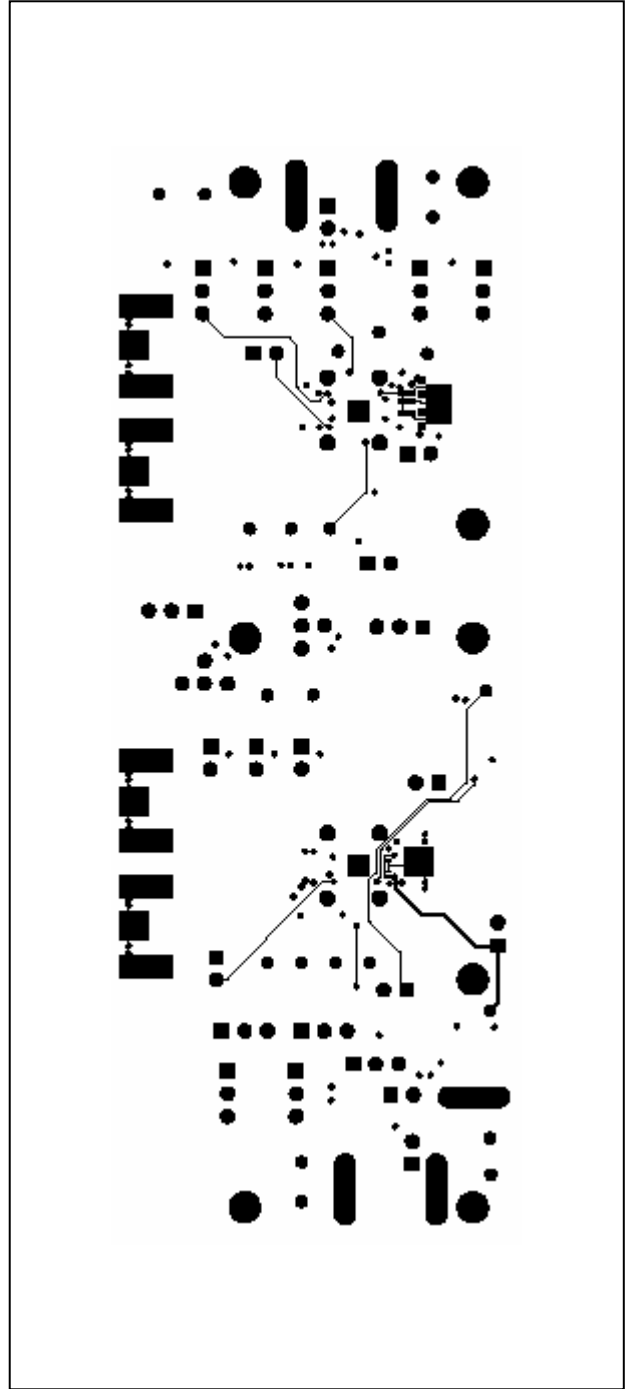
MAX3738 评估板 PCB 布局 — 焊接层
